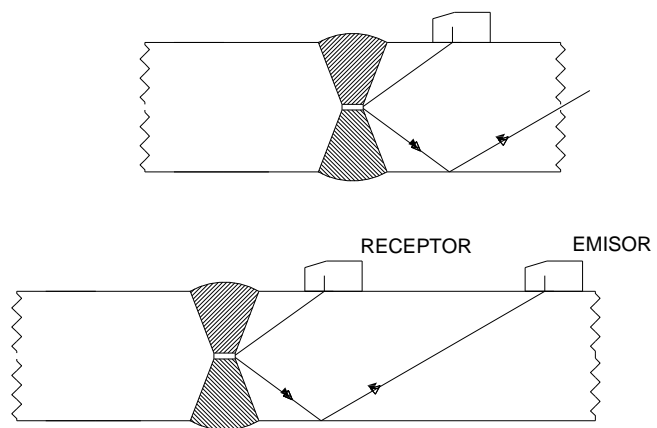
Ubicación frecuente de Falta de Fusión de juntas Soldadas
